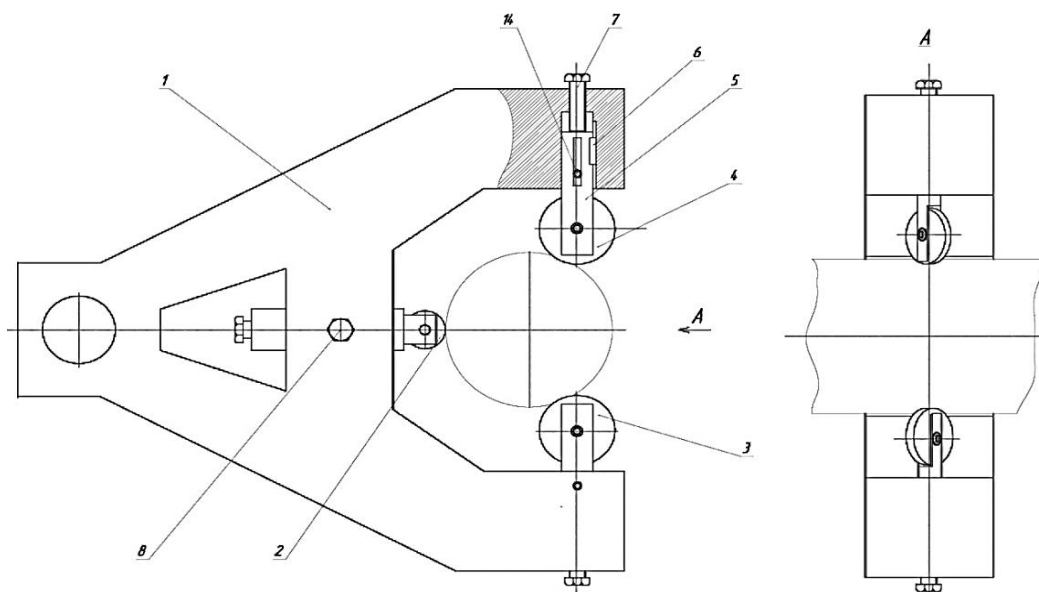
Пристрій для поверхнево-пластичної деформації робочих поверхонь деталей машин
